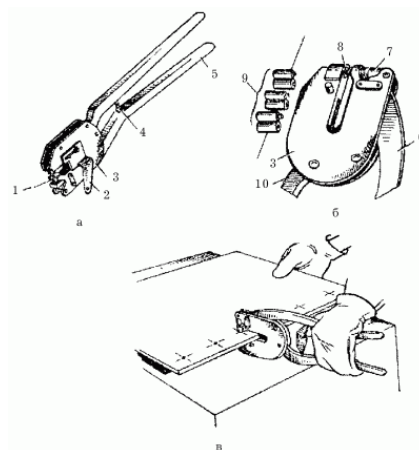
Дырокол (перфоратор): а – общий вид; б – корпус перфоратора с набором пуансонов и матриц; в – пробивка отверстий дыроколом: 1 – подсекатель; 2 – шагомер; 3 – корпус; 4 – возвратная пружина; 5 – ручки; 6 – верхний рычаг; 7 – пуансон; 8 – матрица; 9 – набор пуансонов и матриц; 10 – нижний рычаг.
